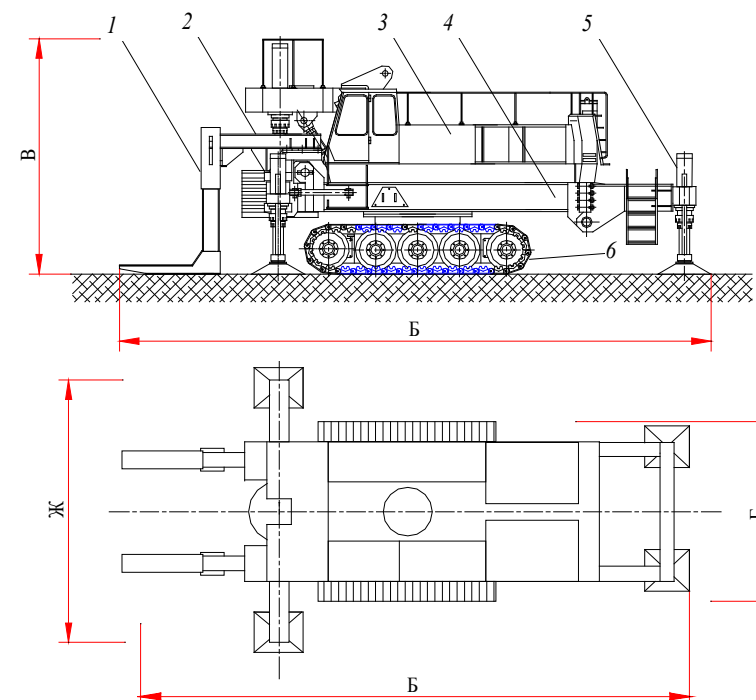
Схема установки УСВ 120 (160): 1 – тяга грузовой платформы; 2 – выносная балка; 3 – силовая установка; 4 – сварная несущая рама; 5 – аутригер задний; 6 – гусеничная ходовая тележка
